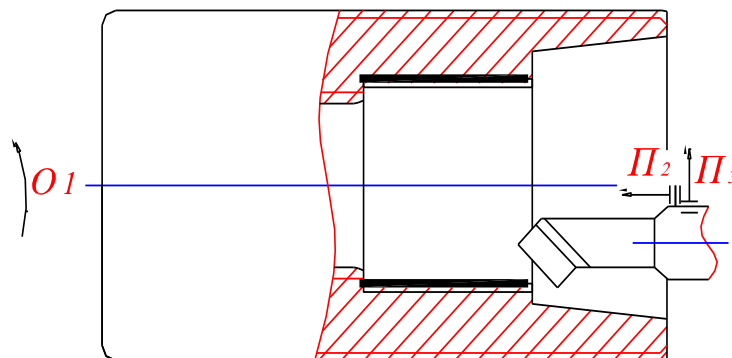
Формоутворення внутрішньої циліндричної поверхні (розточування отвору)
